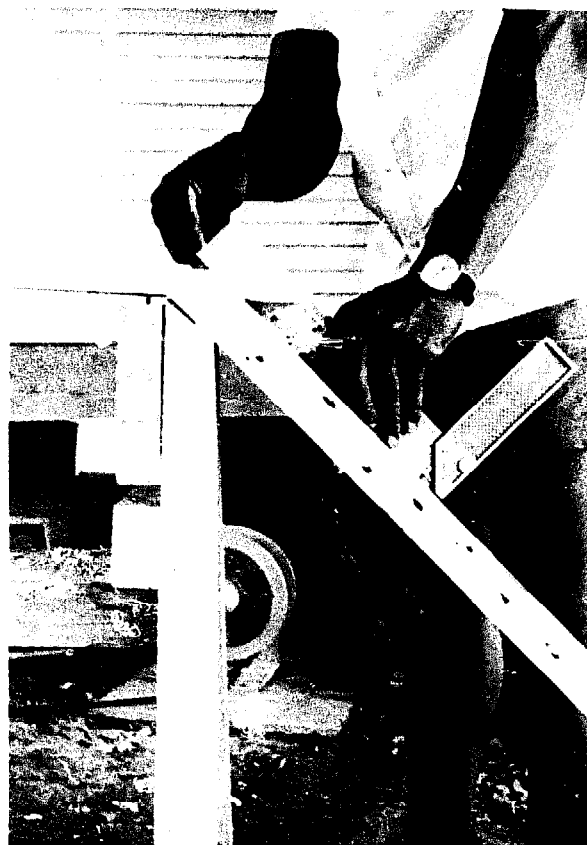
On marquera l'endroit de coupe en tenant une équerre sur le porte-étrave
